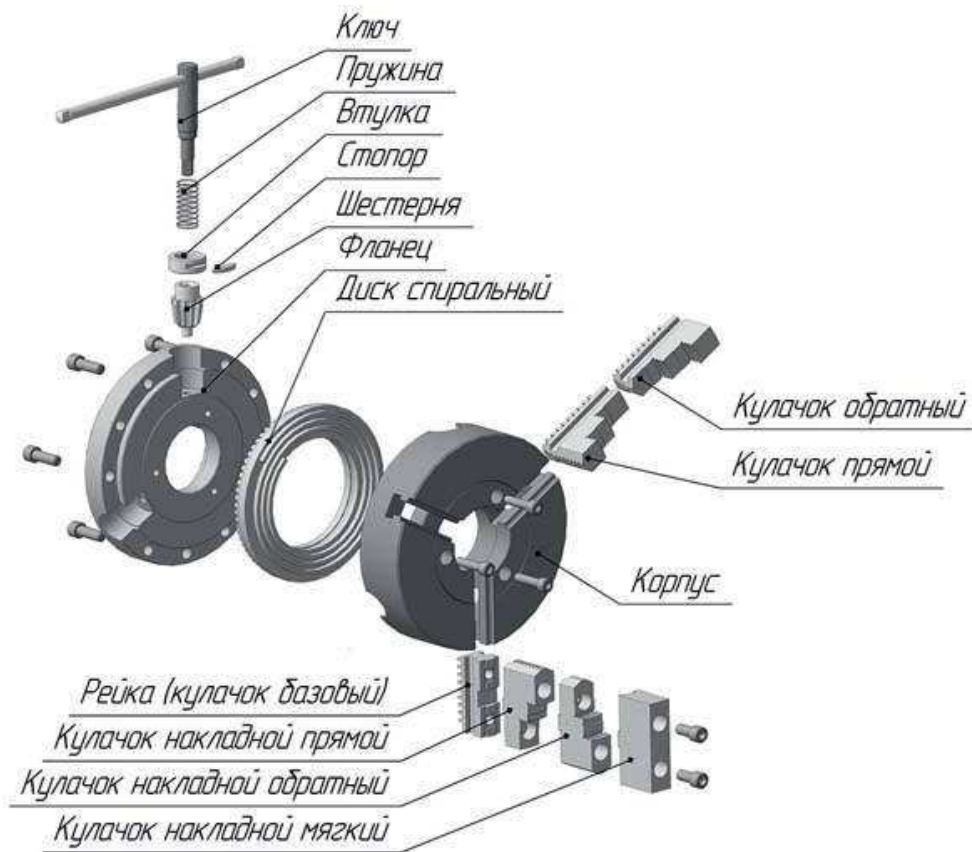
Трикулачковий патрон для токарного верстата
